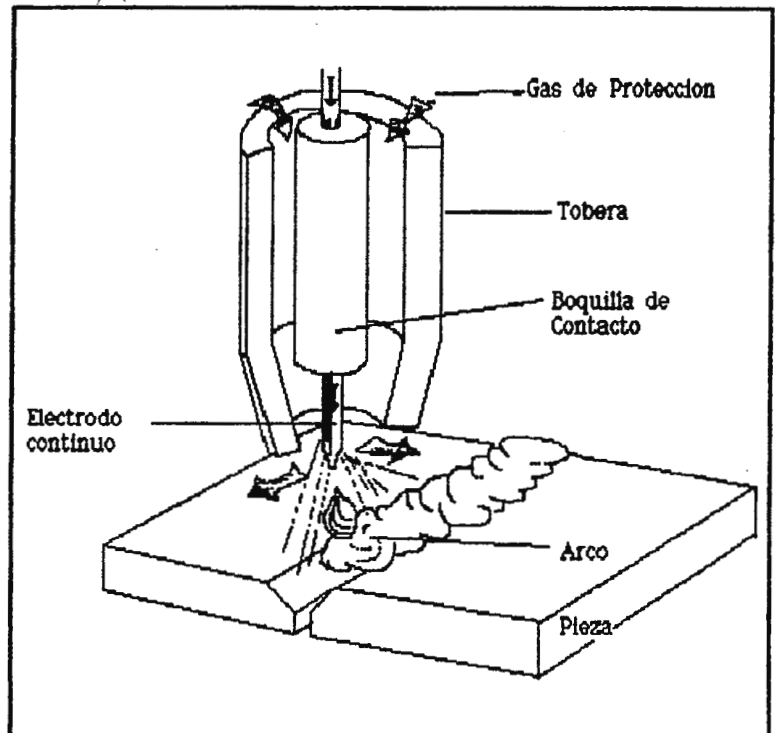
Proceso de Soldadura M.I.G.
